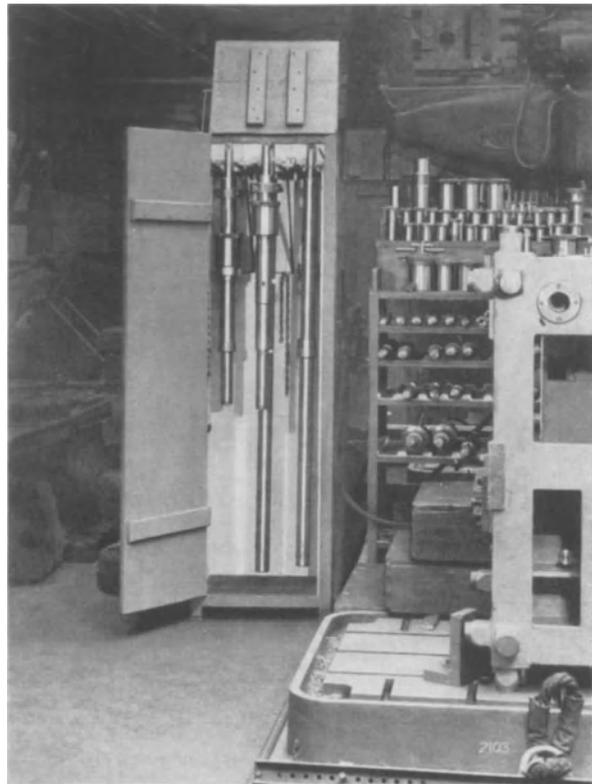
Bohrstangen-Schrank mit aufklappbarem Kopfstück
